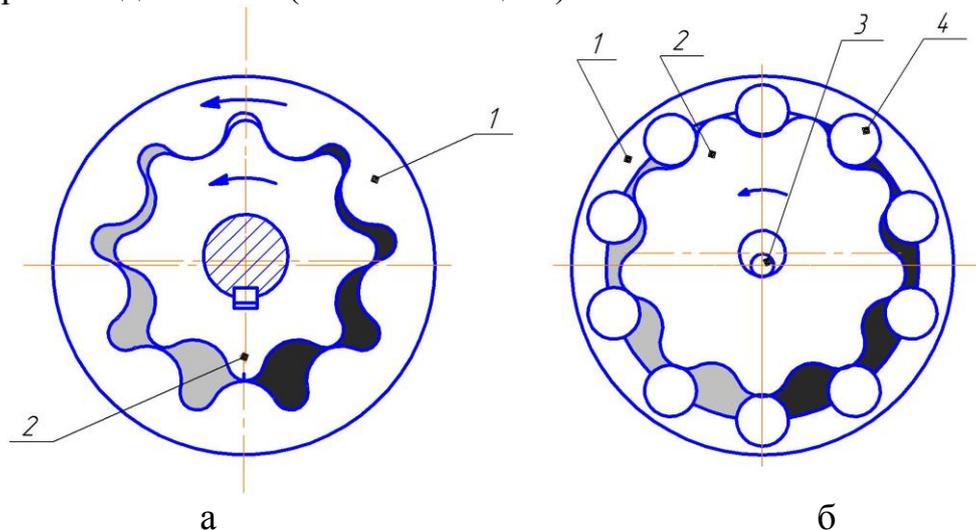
Схемы гидромашин с различным контуром рабочей полости: а – с гипоциклоидальным профилем вытеснителей; б – с круговым профилем вытеснителей; 1 – охватывающий вытеснитель, 2 – охватываемый вытеснитель, 3 – эксцентрики; 4 – зубья.
